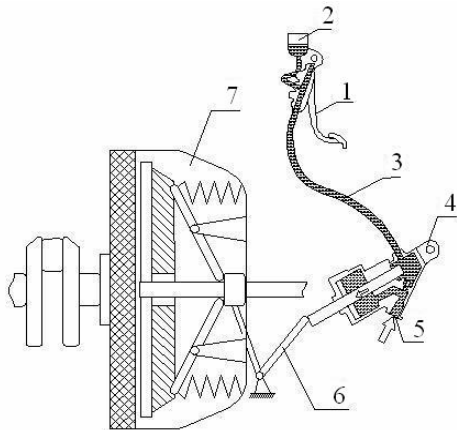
Схема гидравлического привода сцепления, с ПГУ: 1 – педаль; 2 – главный цилиндр сцепления с бачком; 3 – трубопровод; 4 – ПГУ; 5 – подвод сжатого воздуха; 6 – вилка выключения сцепления; 7 – сцепление
